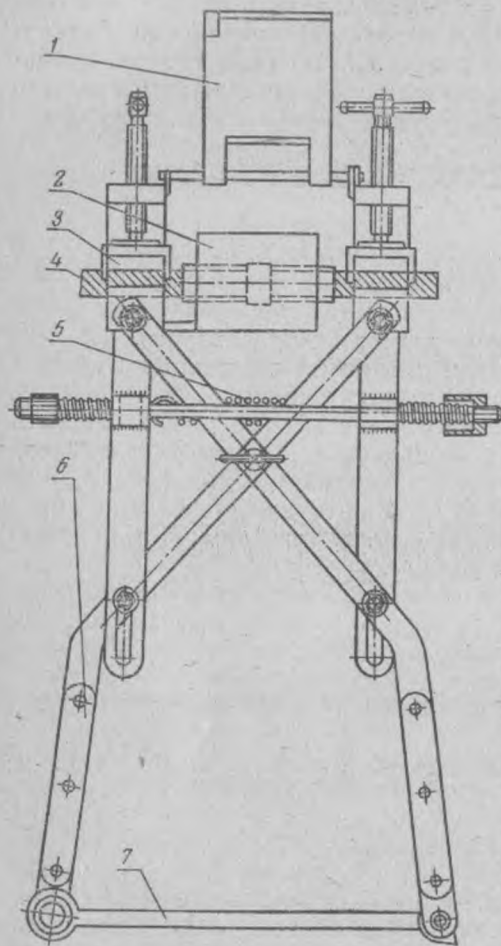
Клещи для термитной сварки проводов
